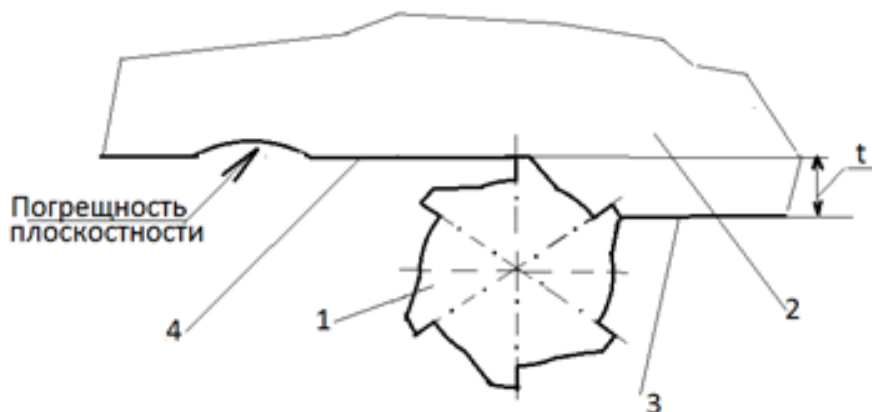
Типовая погрешность плоскостности при фрезеровании длиннокромочной концевой фрезой: 1 - фреза; 2 - деталь; 3 - обрабатываемая деталь; 4 - обрабатываемая поверхность t - припуск под фрезерование.
